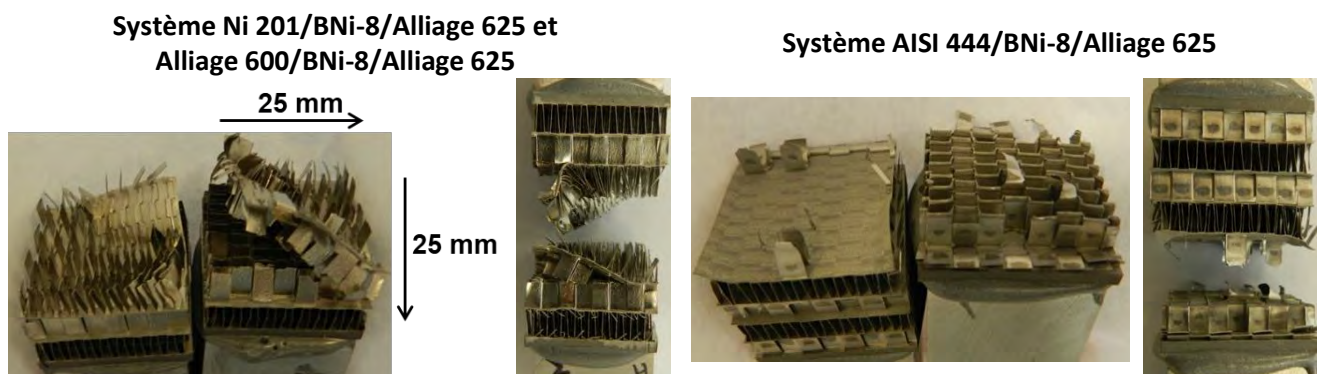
Surfaces de rupture des éprouvettes de traction
